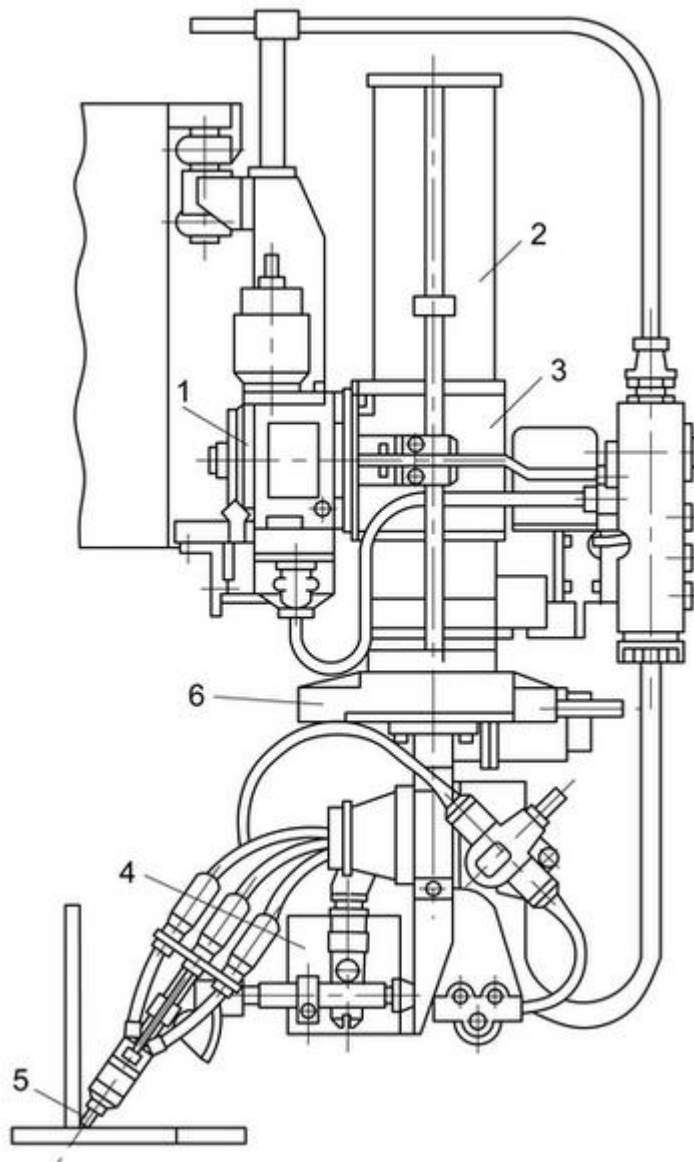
Сварочный автомат А-1411Г.
